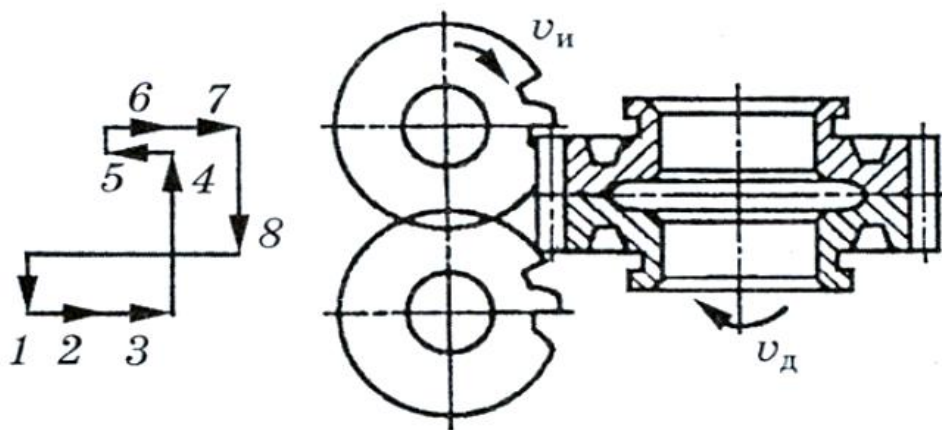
Схема двухпроходного зубофрезерования: 1,2 – ускоренный подвод фрезы; 2-3 – медленная подача фрезы; 3-4 – рабочая подача первого прохода; 4-6 – ускоренный отвод и подвод фрезы; 7-8 – рабочая подача второго прохода; 8-1- ускоренный отвод фрезы
